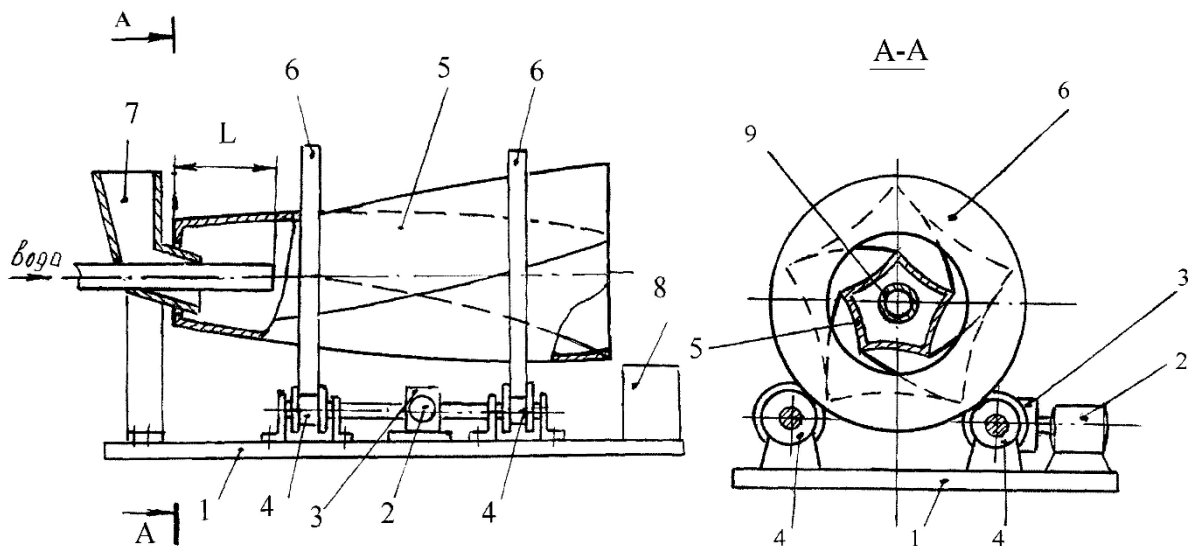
Смеситель с дополнительными рабочими элементами
